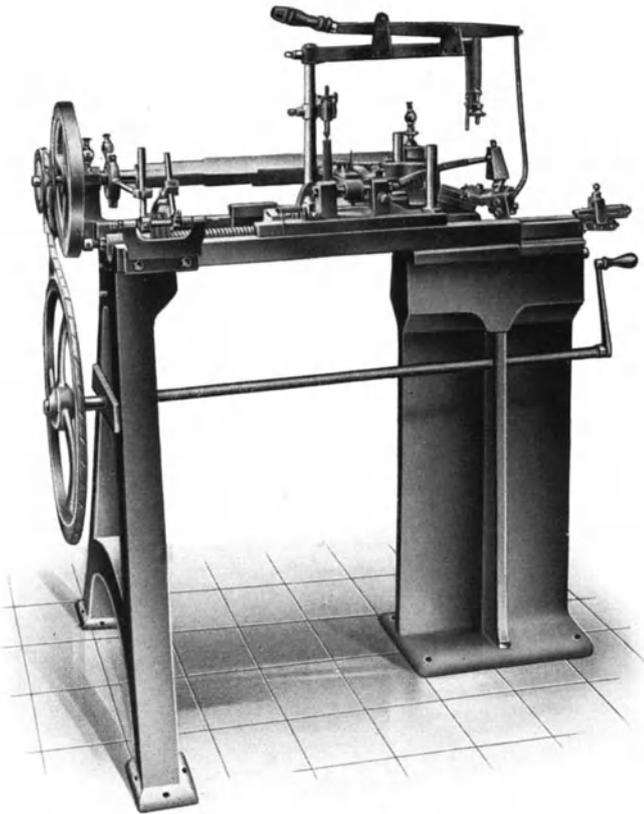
Schweizerische Haumaschine, 1880. (Erste in Deutschland aufgestellte Maschine für Uhrmacherfeilen.)
